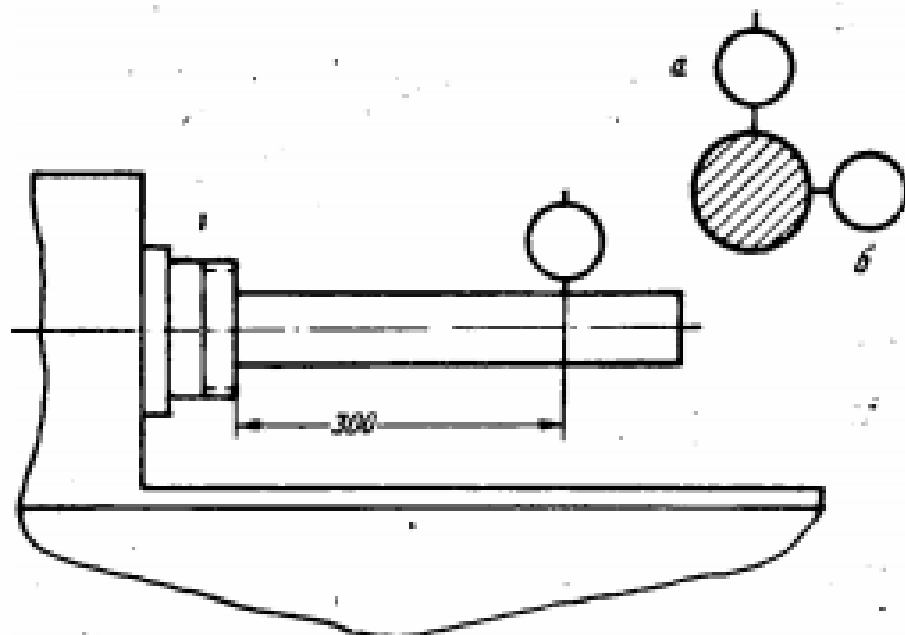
Схема проверки параллельности оси шпинделя направлению движения каретки
